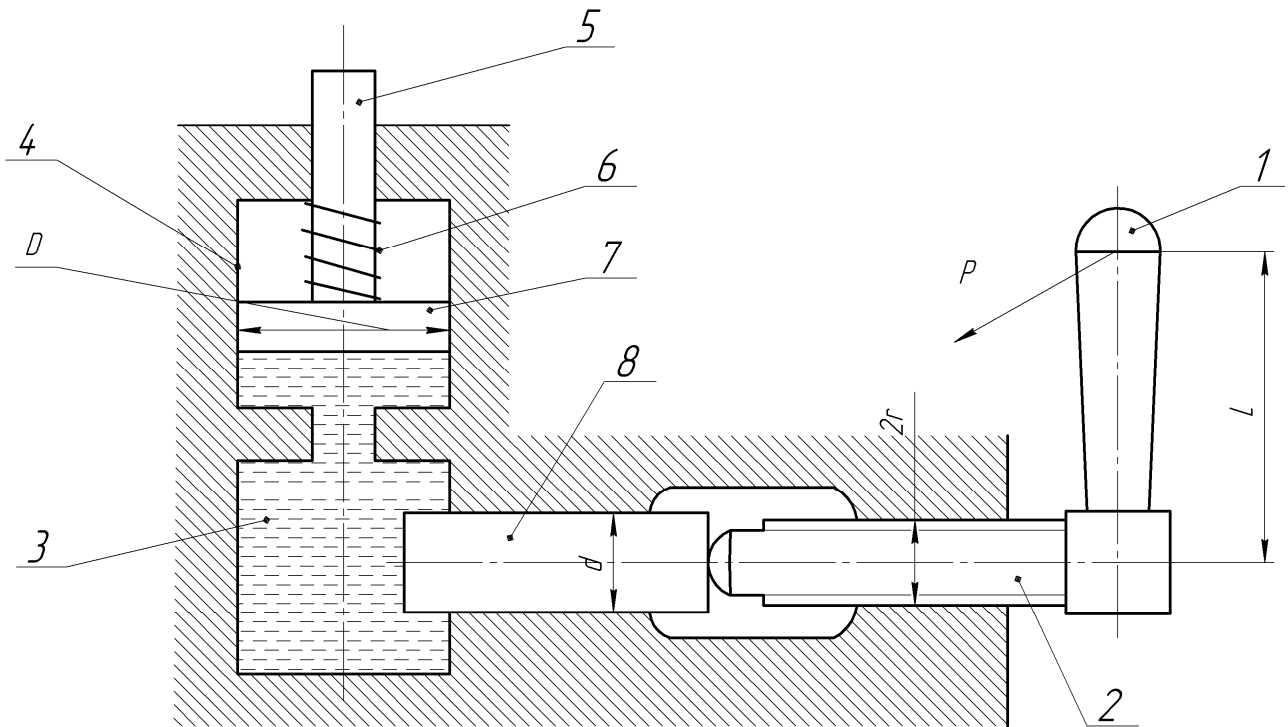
Будова та параметри механогідравлічного приводу: 1 – ручка; 2 – гвинт; 3 – резервуар; 4 – циліндр; 5 – шток; 6 – пружина; 7 – поршень; 8 – плунжер; Q – сила на штоку гідроциліндра; P – зусилля на рукоятці; d – діаметр плунжера; L – довжина рукоятки; r – радіус гвинта; D – діаметр поршня
